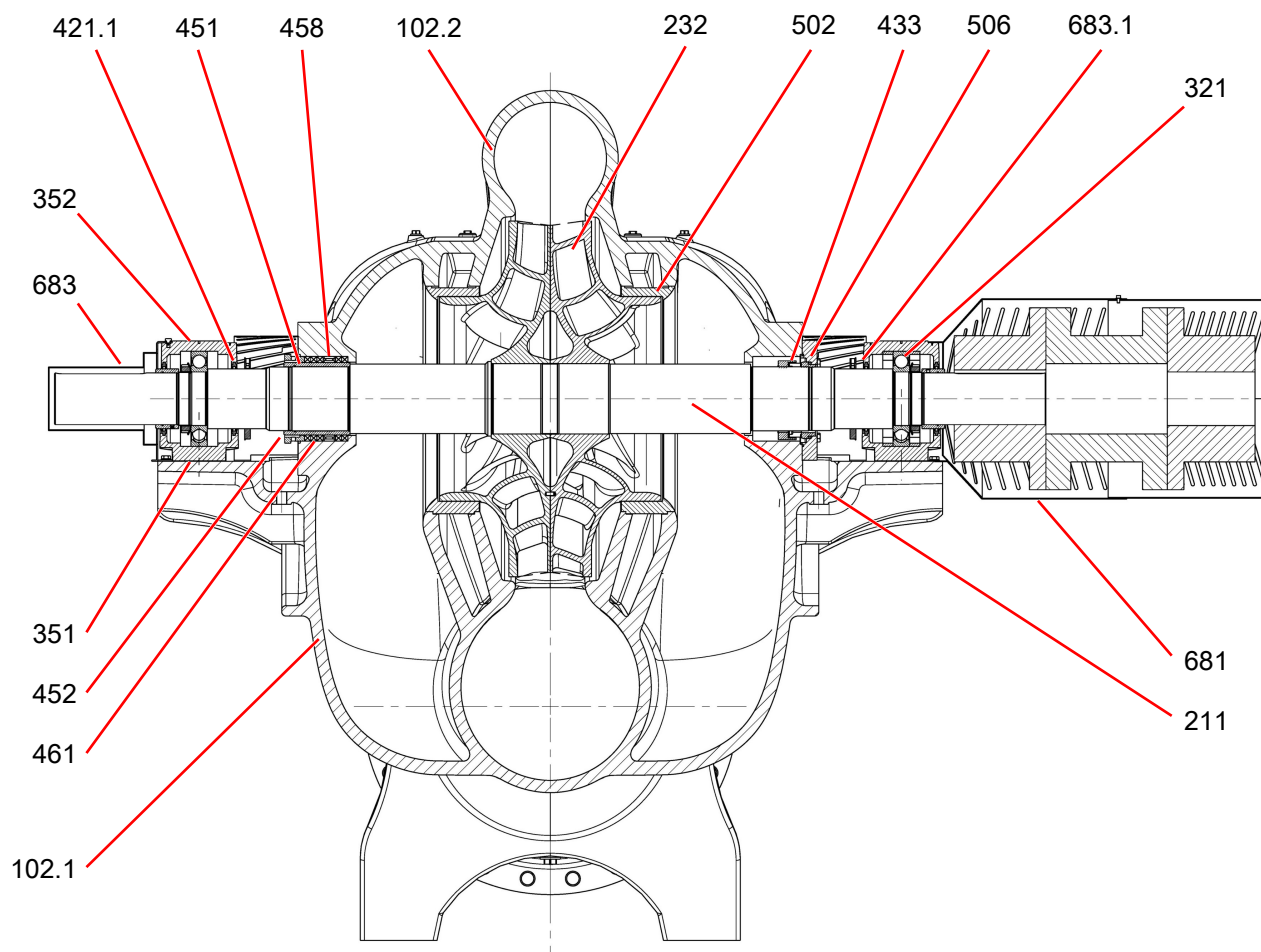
Чертеж насоса ASP-A.S в разрезе (смещенные лопасти рабочего колеса, прессовая посадка)
